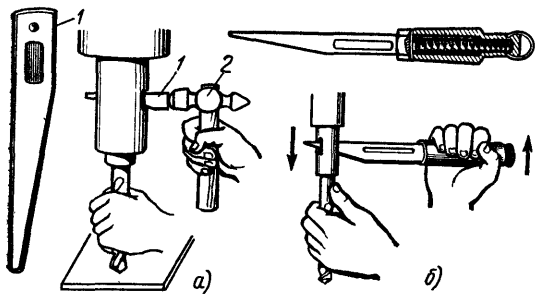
Удаление сверл (или патрона со сверлом) из шпинделя станка:
